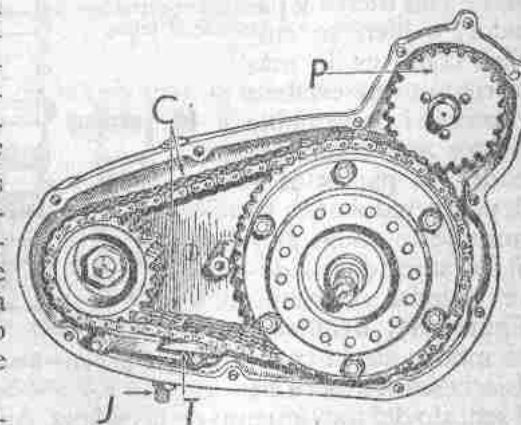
Tensor de la cadena primaria en caso de bloque motor.
